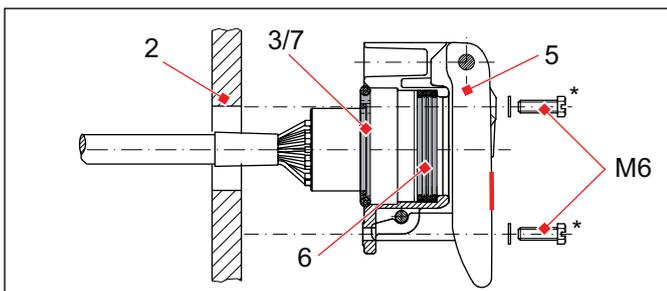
Kupplungsdose mit Crimpadapter und Wechseleinsatz an Fahrzeugwand anschrauben
